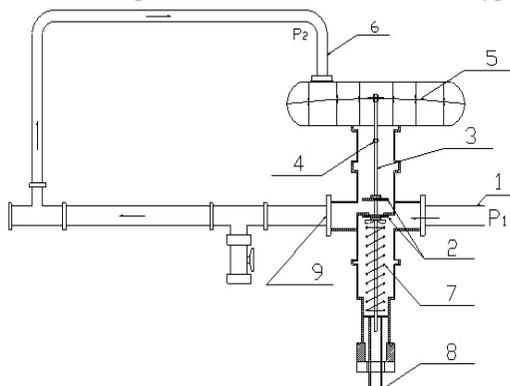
Схема РД: 1. Входной патрубок; 2. Запорный клапан; 3. Шток; 4. Пускатель; 5. Мембрана; 6. Импульсная трубка; 7. Пружина запорного клапана; 8. Регулировочный шток; 9. Выходной патрубок
